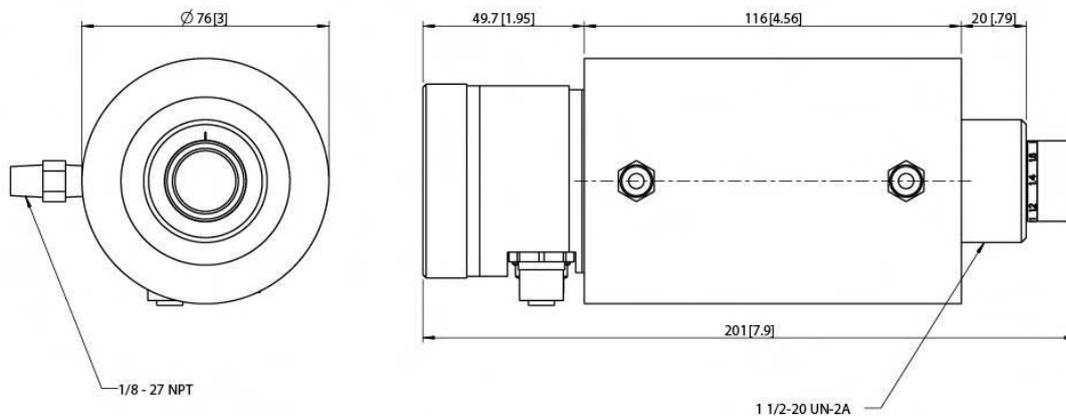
Dimensions d'un capteur Endurance® avec boîtier de refroidissement
